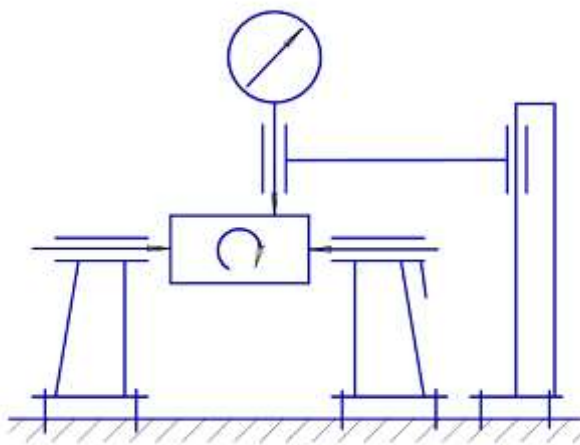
Базування за принципом суміщення установочної та вимірювальної бази
